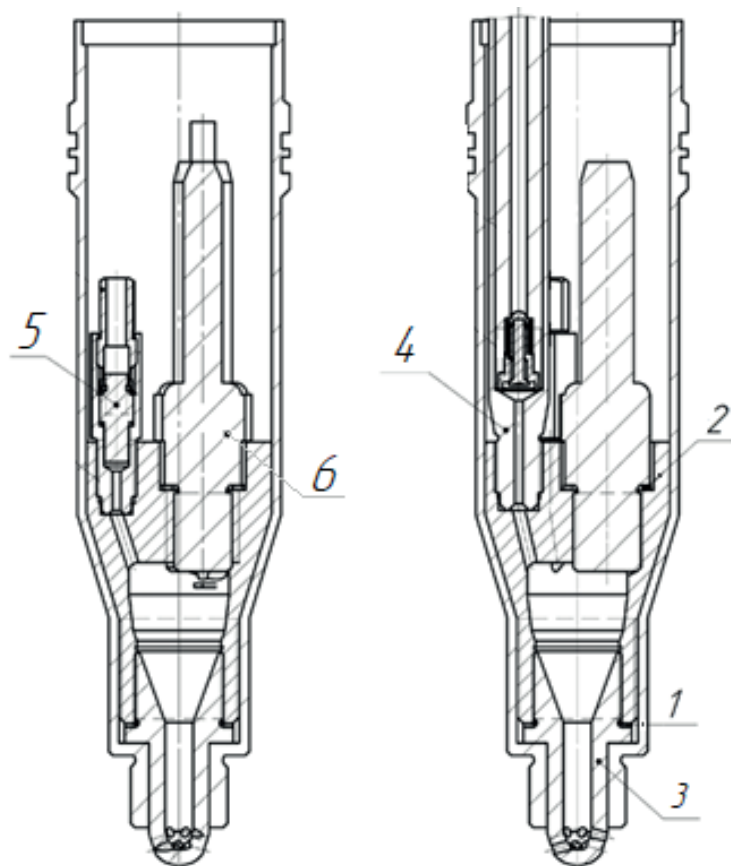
Активная форкамера для газопоршневого двигателя ГПД-185
